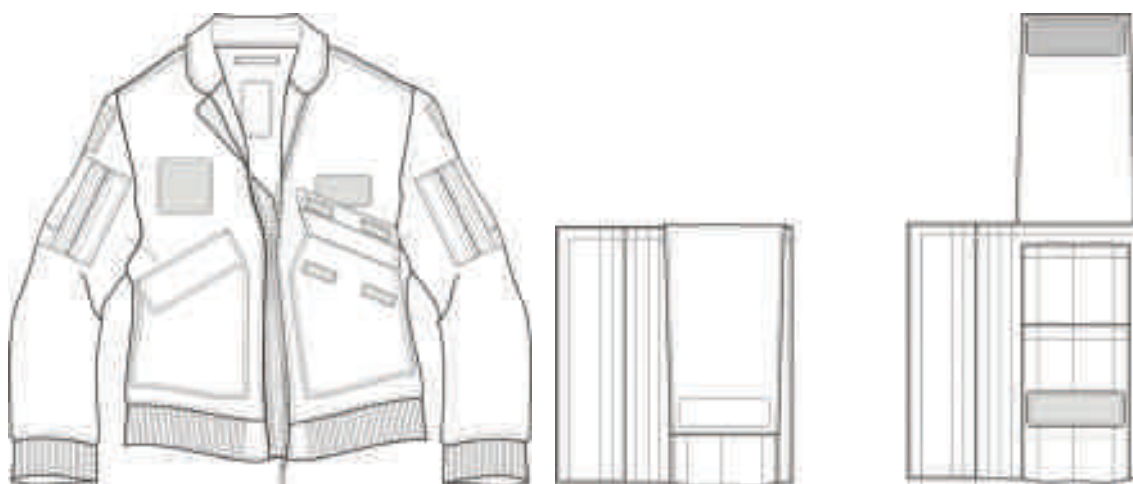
exemplo de desenho técnico e de desenho de pormenor (blusão FAP)
